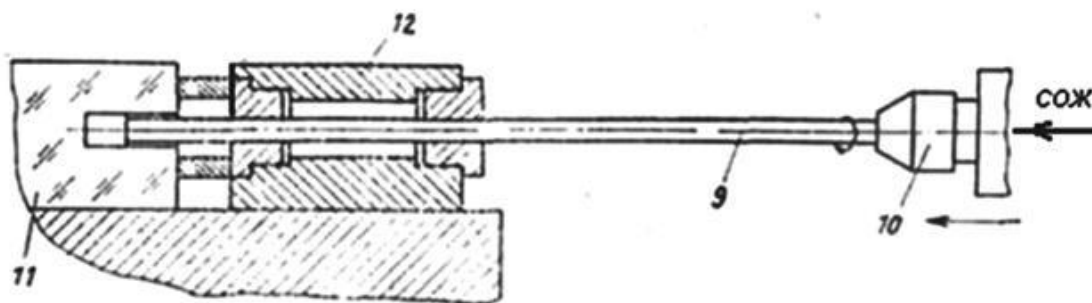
Схема алмазного свердління глибоких отворів з обертанням інструмента
